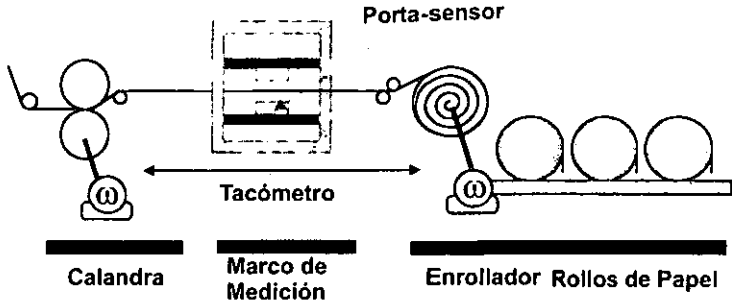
Requerimientos en la sección de calandreo y enrollador.
